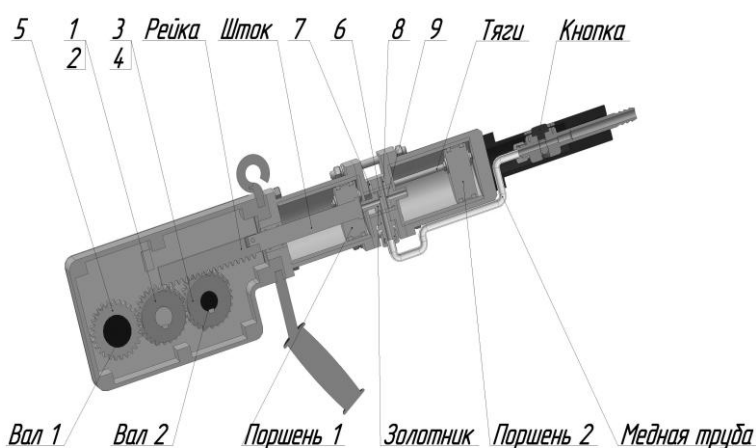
3D-модель модернизированного пневматического гайковерта
